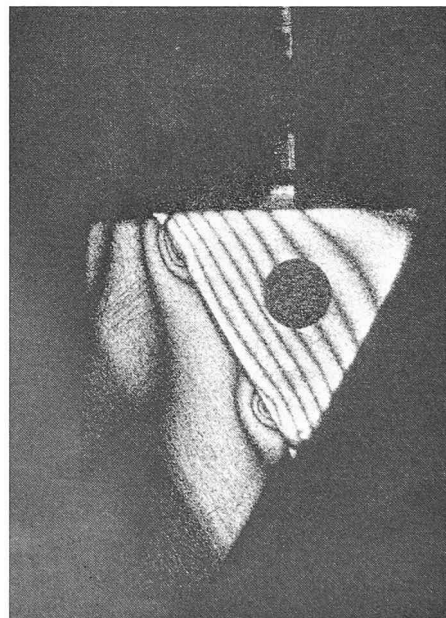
Déformations transversales du porte-outil et de la plaquette, dues au serrage du pion.
